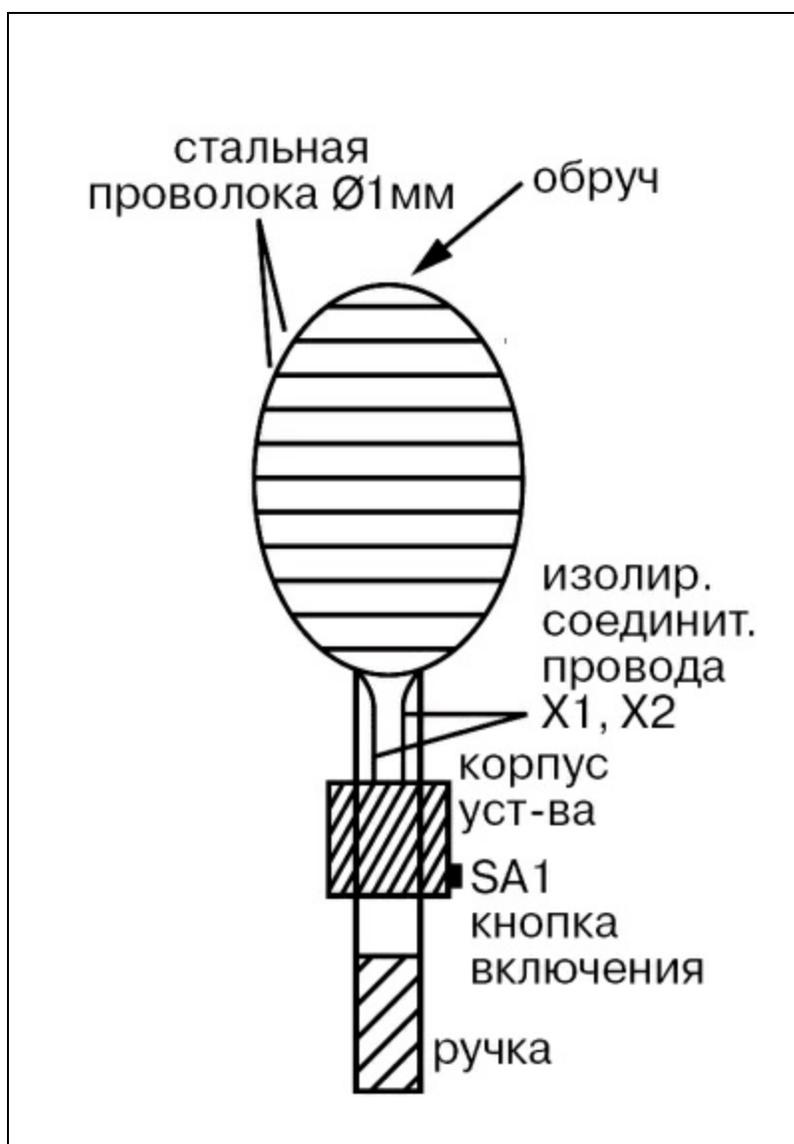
Конструктивная схема переделки ракетки для игры в бадминтон
